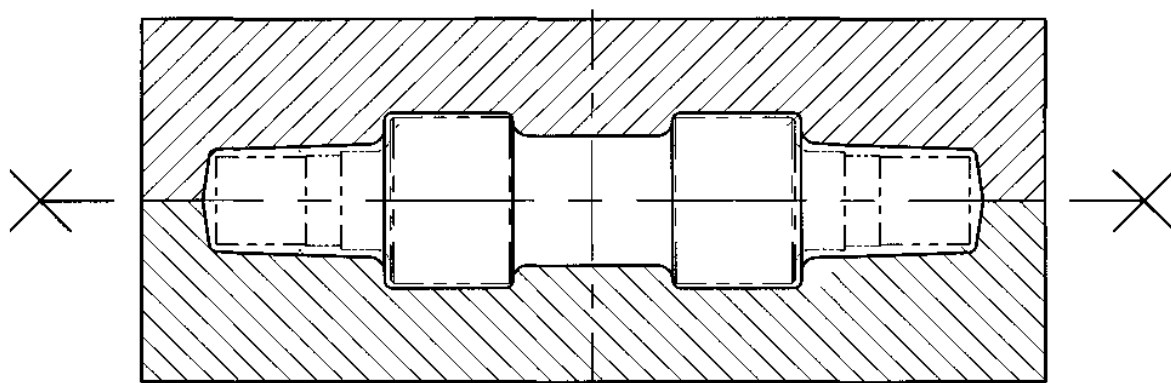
Схема заливки: 1- литники; 2-отливка; 3-верхняя полуформа; 4- нижняя полуформа; 5- выпоры.
